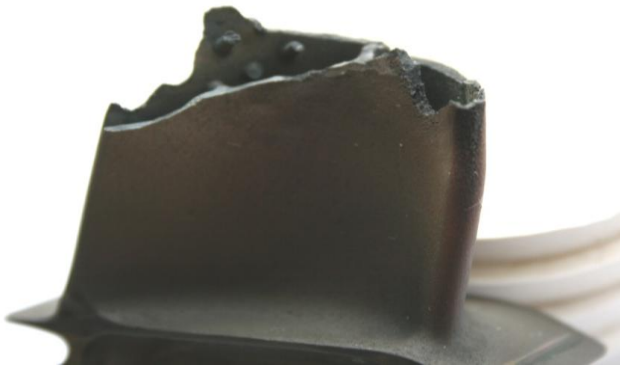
Розтріскування поверхні лопатки поблизу зламу
